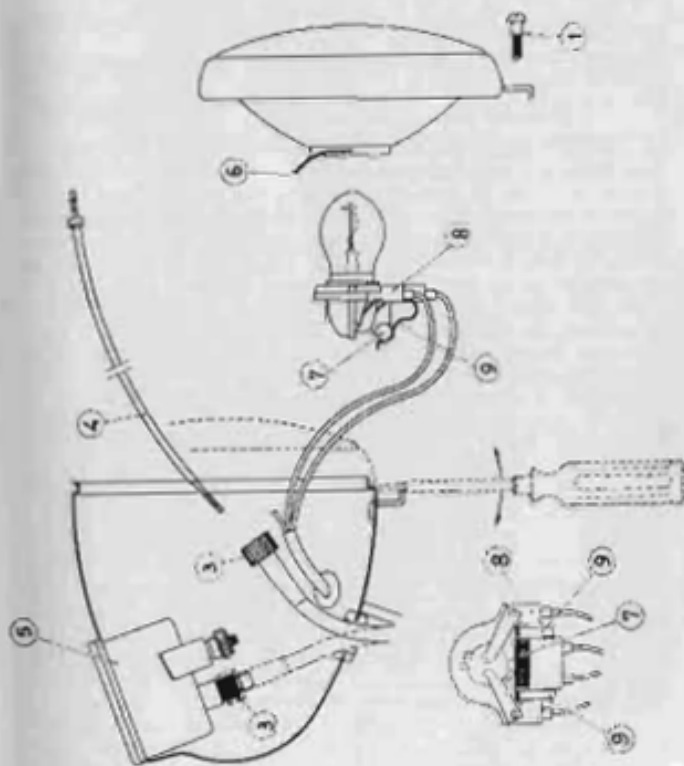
Faro delantero. Desmontaje del cable transmisión puerta-kilómetros y cambio de lámpara.
